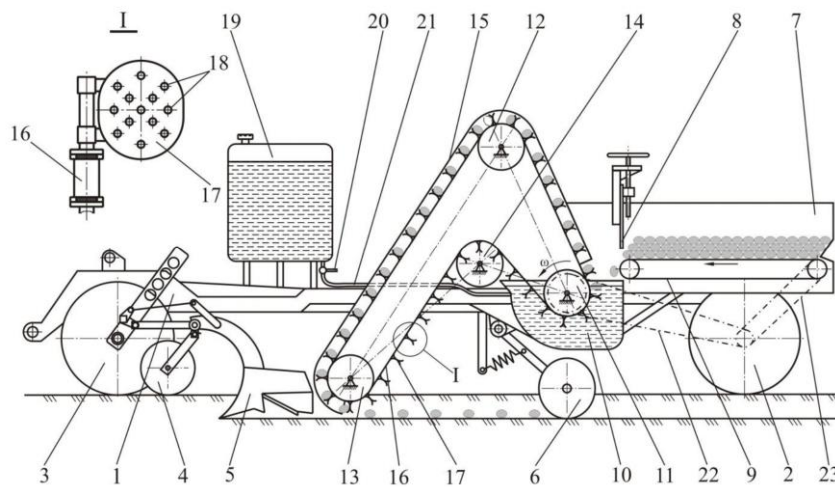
Картоплесаджалка: 1 – рама; 2 – колесо опорне-приводне заднє; 3 – каток опорний; 4 – колесо копіювальне; 5 – сошник-борозоутворювач; 6 – загортач; 7 – бункер насіннєвих бульб; 8 – заслінка бункера; 9 – донний транспортер; 10 – живильний ківш, 11 – ведуча зірочка; 12, 13, 14 – ведені зірочки; 15 – кожух; 16 – елеваторний транспортер; 17 – ложечка; 18 – дренажні отвори; 19 – резервуар робочого розчину; 19 – колесо копіювальне; 20, 21 – гідравлічні комунікації; 22, 23 – ланцюгова передача.
